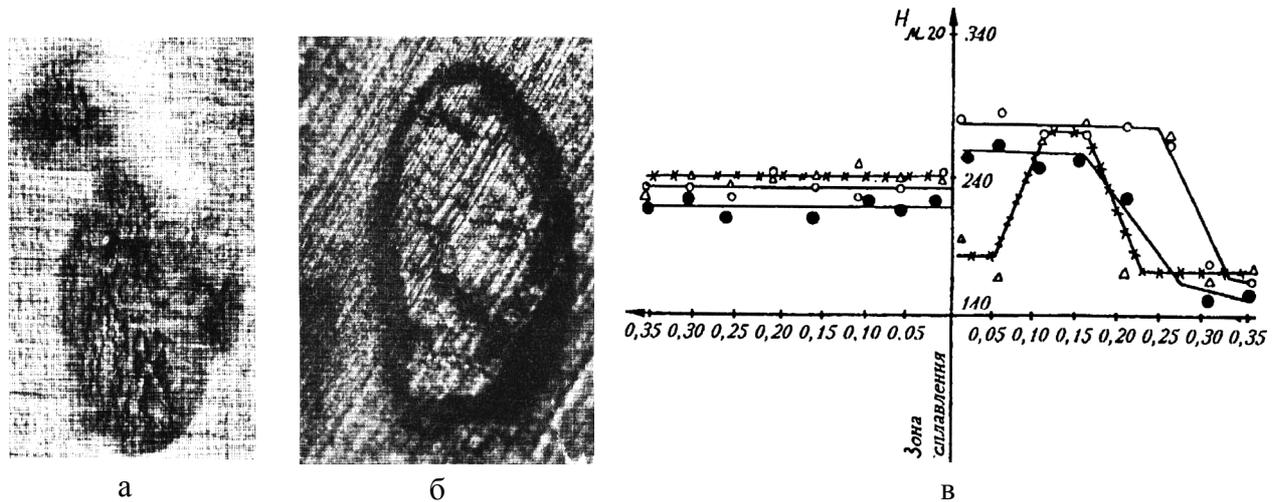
Межкристаллитная коррозия в брызгах металла, прилипших к поверхности стали Х18Н9Т ($\times 50$): при РДС (а), при сварке в CO_2 (б) и микротвердость граничной зоны капли с поверхностью основного металла (в)
